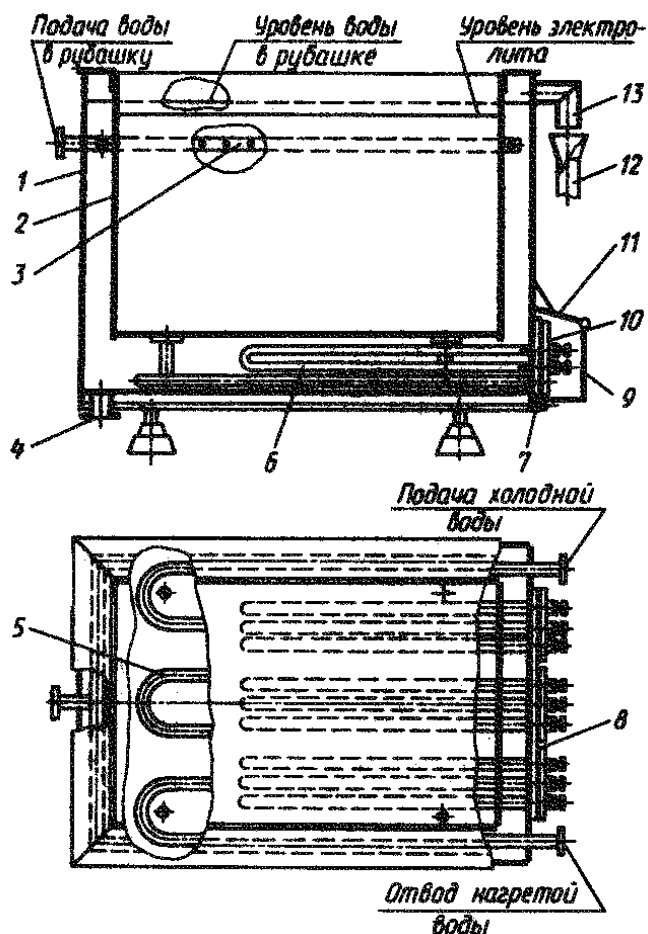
Ванна с водяной рубашкой и электронагревом: 1 – наружная ванна; 2 – рабочая ванна; 3 – труба подачи холодной воды в рубашку; 4 – патрубок слива воды из рубашки; 5 – змеевик охлаждения; 6 – электронагреватель; 7 – пластина; 8 – уплотнительная прокладка; 9 – крышка; 10 – фланцы электронагревателей; 11 – защитный козырек; 12 – воронка; 13 – сливной патрубок
